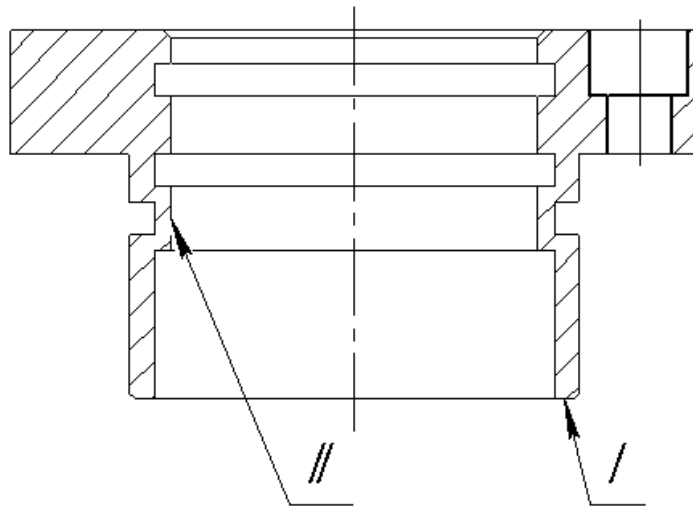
Зображення поверхонь деталі, що використовуються при базуванні
